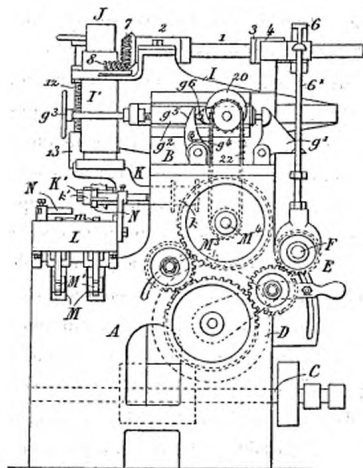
Machine à moulurer Van Houten, vue par l'extrémité.
